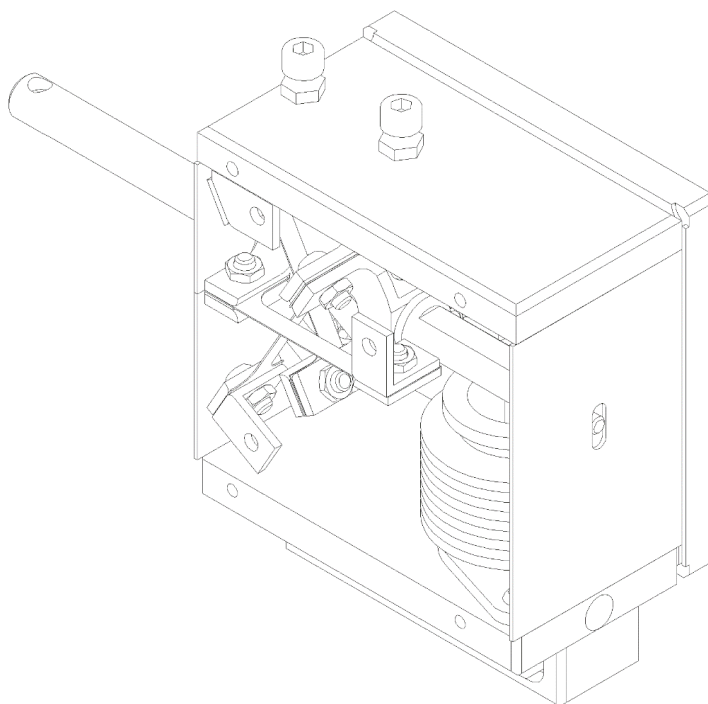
Общий вид приспособления, для обработки отверстий малого диаметра.
